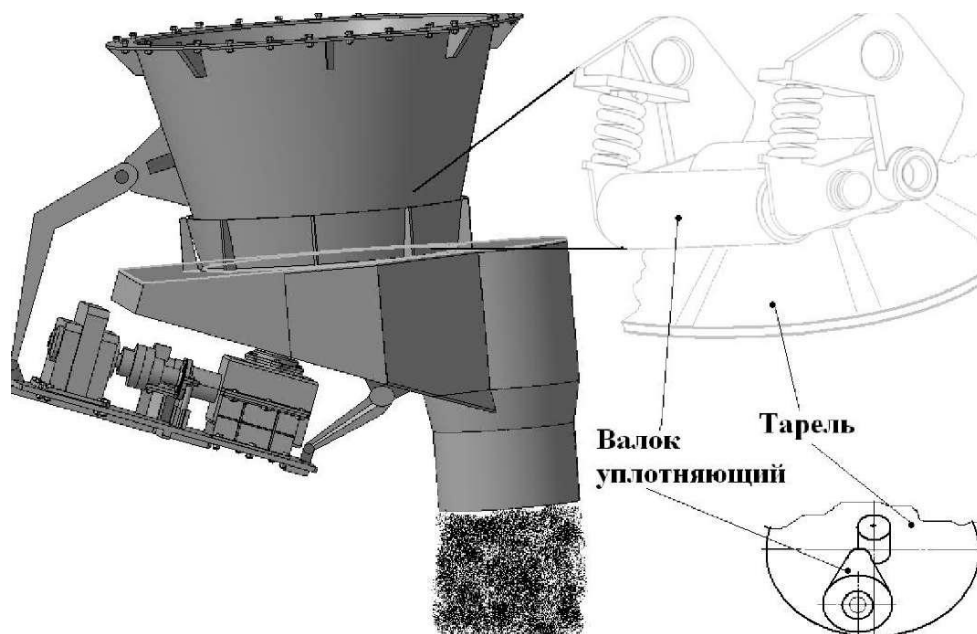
Тарельчатый питатель углезагрузочной машины с подпрессовкой материала между валком и тарелью.
